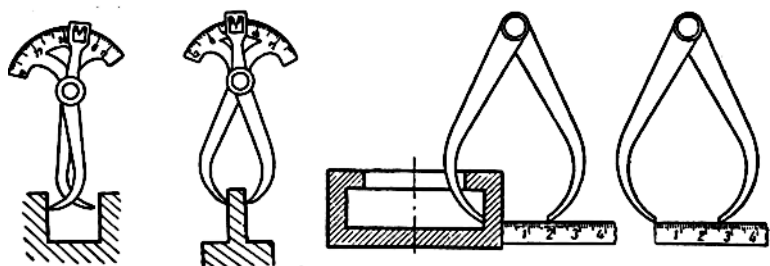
Různá universální měřidla, jichž se používá v kovoprůmyslu.
